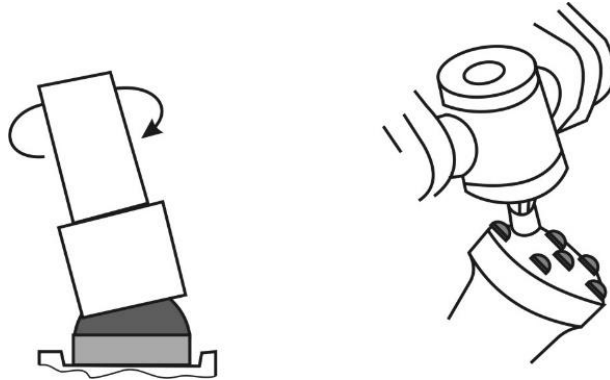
Спосіб реконструювання твердосплавної напайки
